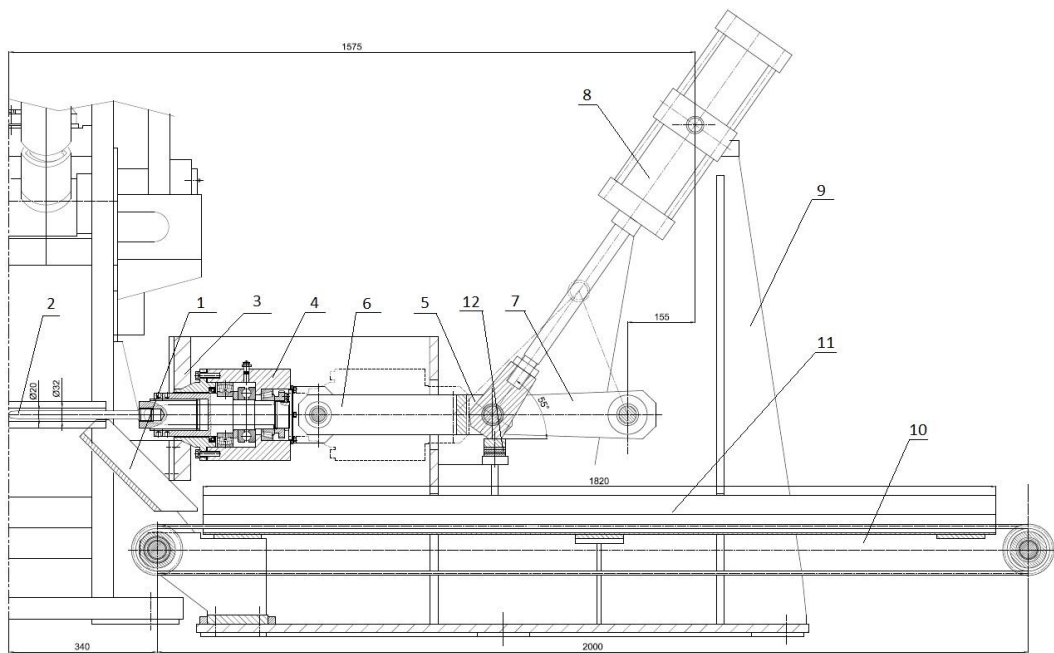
Выходная сторона прошивного стана: 1 – наклонный желоб; 2 – стержень с оправкой; 3 – упорная плита; 4 – упорная головка; 5 – рычажный механизм; 6, 7 – рычаги; 8 – пневмопривод; 9 – рама для пневмопривода; 10 – транспортер; 11 – рама; 12 – демпфирующее устройство
